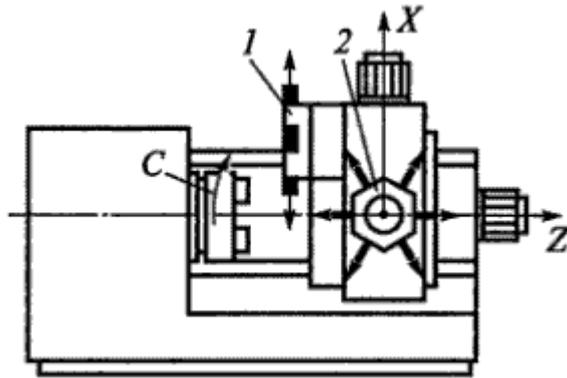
Токарный станок с ЧПУ (1 и 2 револьверные головки)
